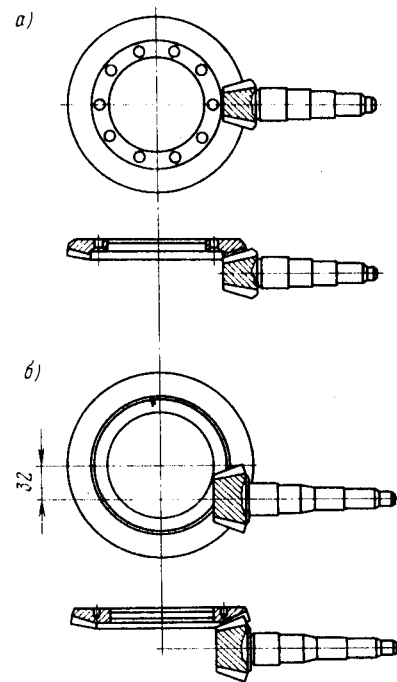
Косозубые конические (а) и гипоидные (б) шестерни главной передачи
